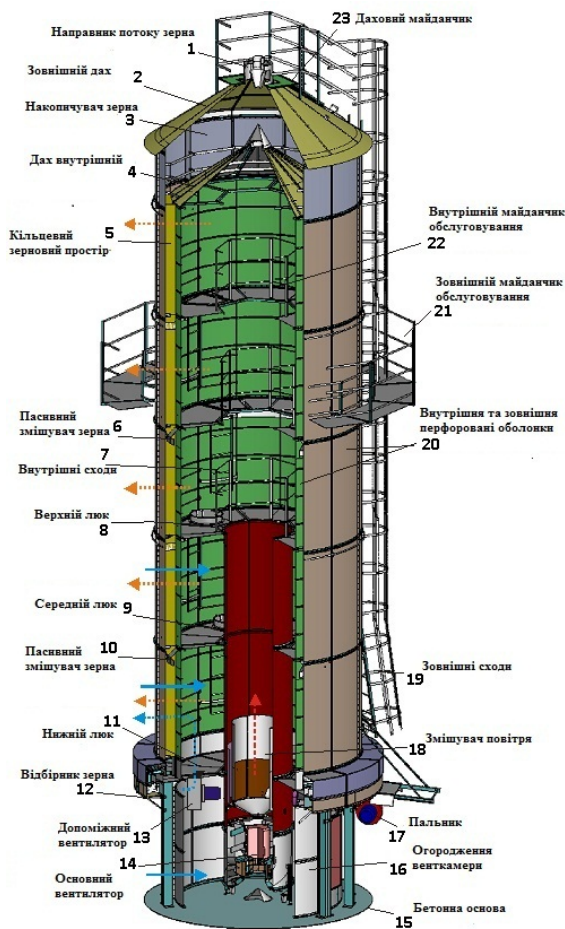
Конструкція баштової сушарки фірми "Астра"
